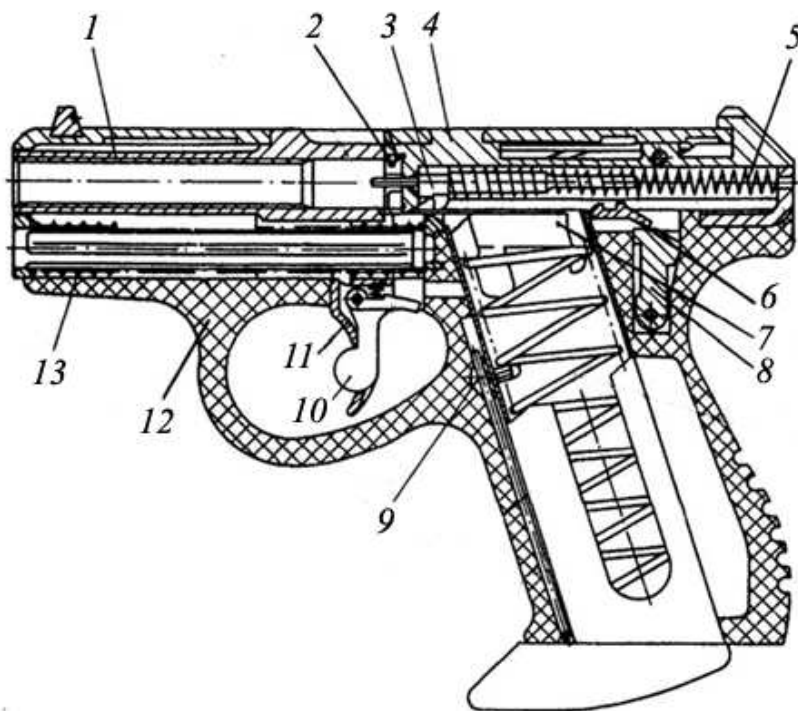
Устройство пистолета: 1 – ствол; 2 – выбрасыватель; 3 – ударник; 4 – кожух-затвор; 5 – боевая пружина; 6 – шептало; 7 – подаватель; 8 – затворная задержка; 9 – защелка магазина; 10 – автоматический предохранитель; 11 – спусковой крючок; 12 – рамка; 13 – возвратная пружина
